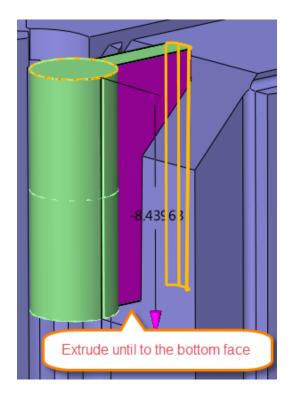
Extrusión del boceto hasta que la cara inferior de electrodo 5
